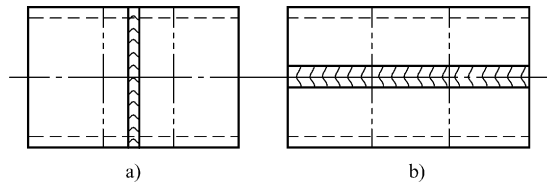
熔焊管接头压扁样坯截取位置
